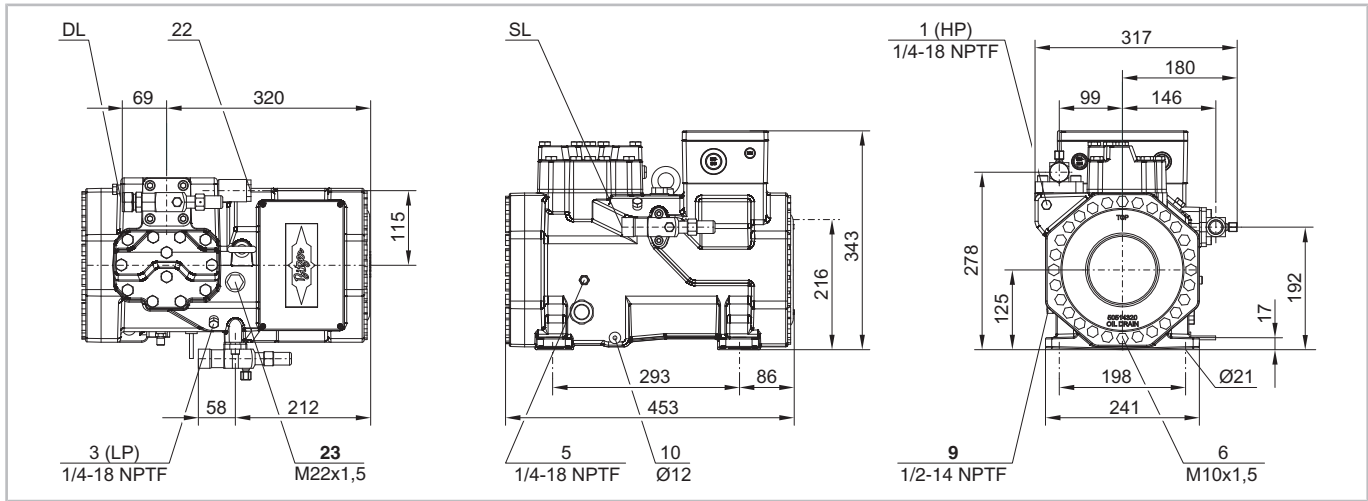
Maßzeichnung 2MTE-4K .. 2KTE-7K
